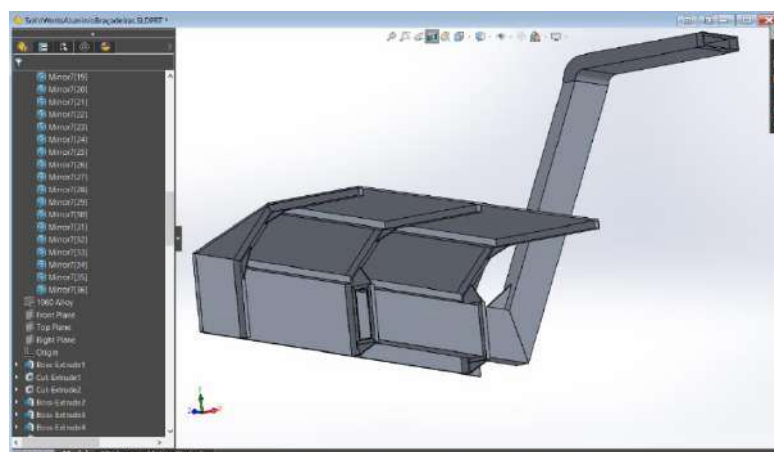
Vista de secção longitudinal da plataforma central e mastro apoiado nesta
